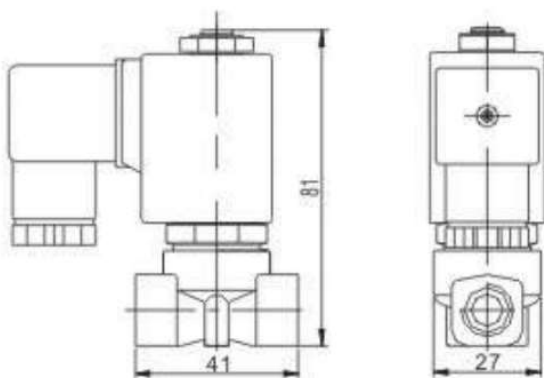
Габаритные и присоединительные размеры клапана типа EV210WR
